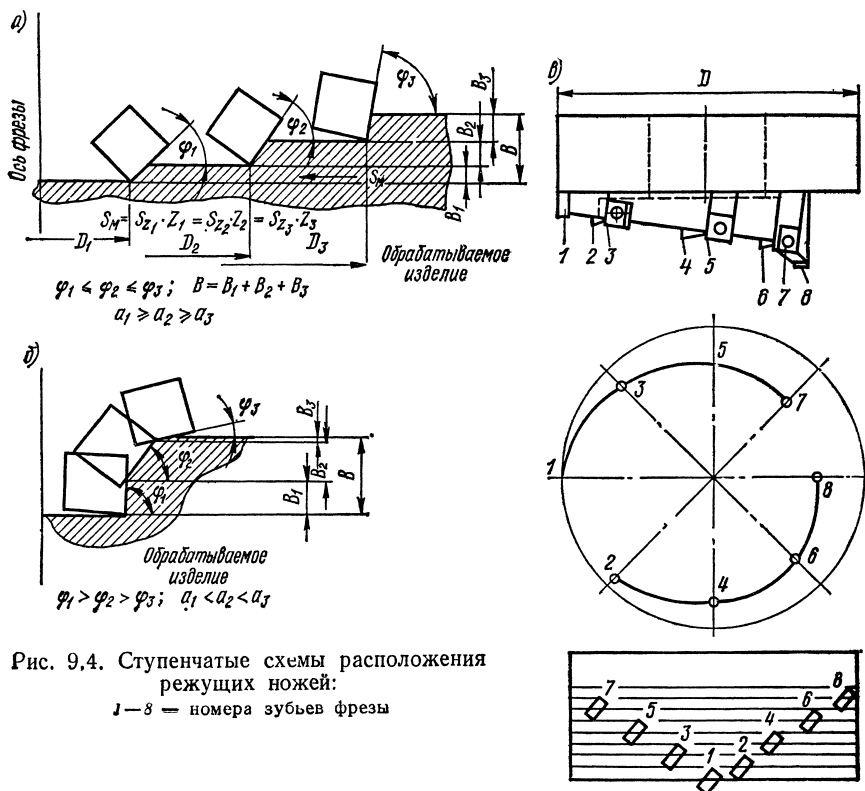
Ступенчатые схемы расположения режущих ножей:
